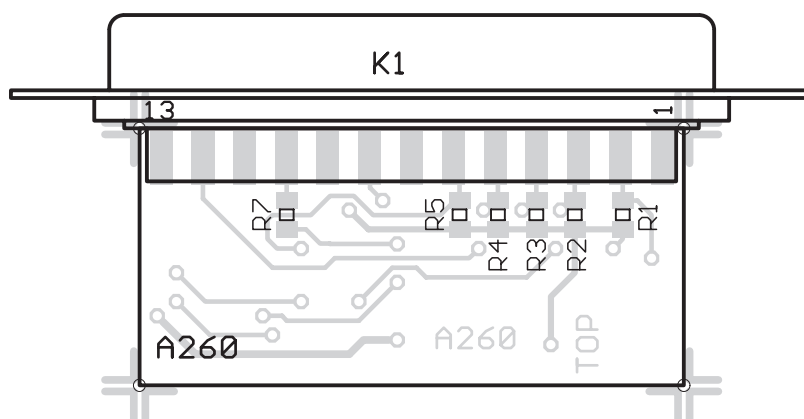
Obrazec desky spojů - strana spojů - BOTTOM (M1:1)
